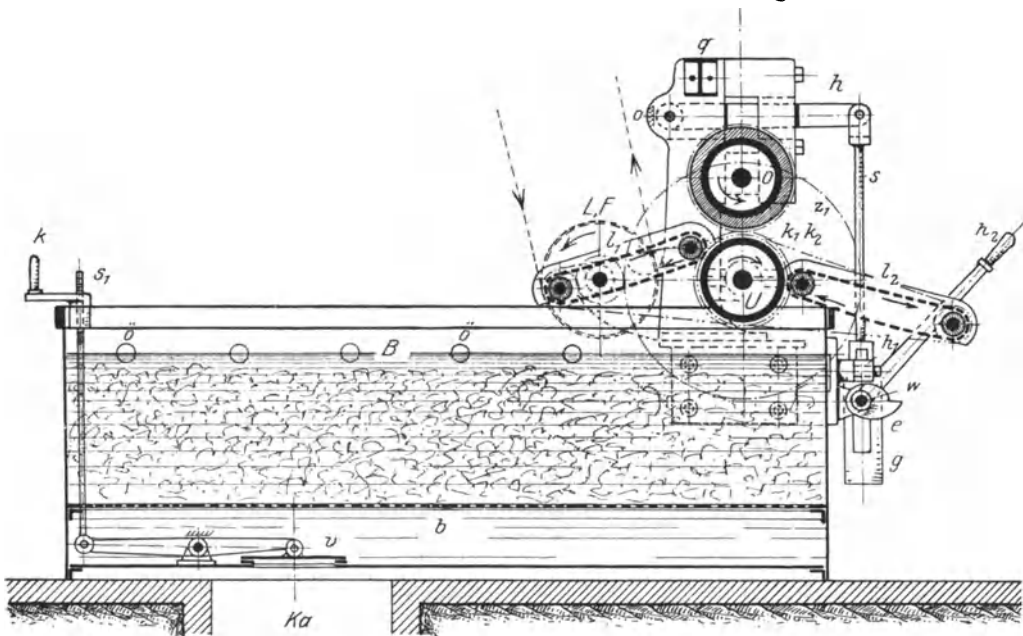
Doppelter Entschweißbottich mit Quetschwerk.
